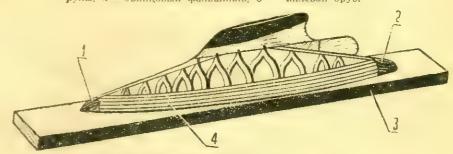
Корпус на станель-доске: 1 — посовая бобышка; 2 — кормовая бобышка; 3 — станель-доска; 4 — общивка.
